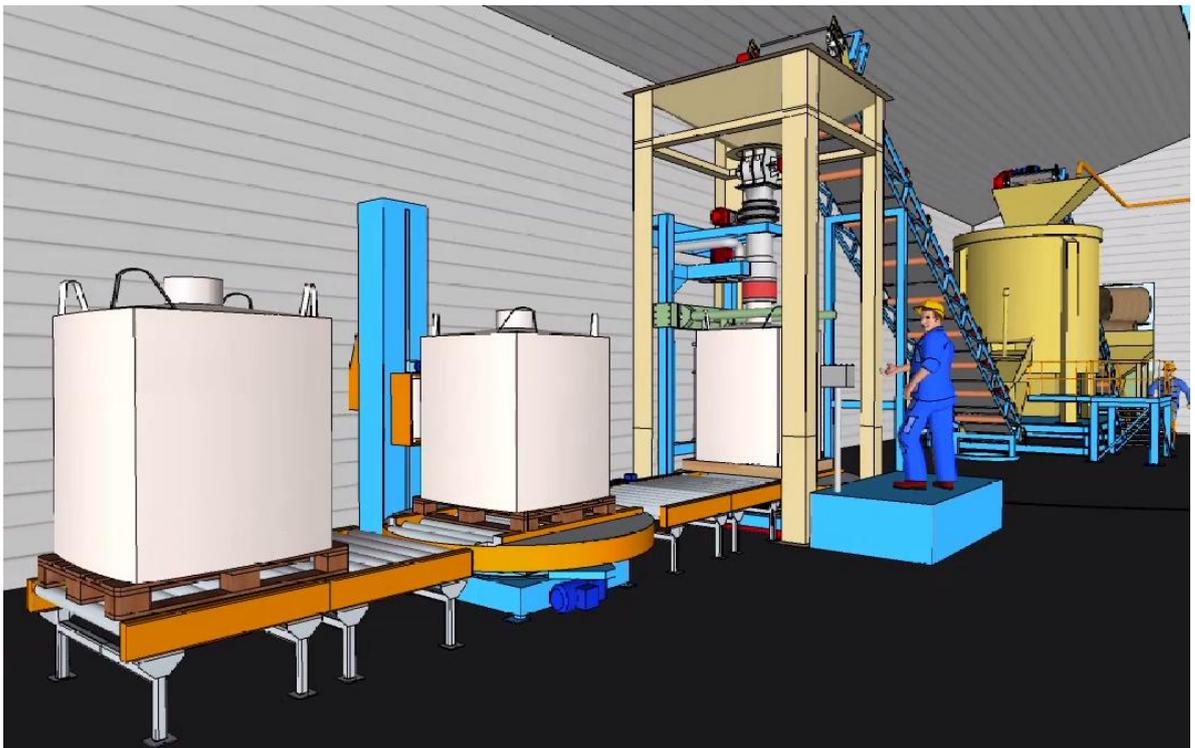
Общий вид фасовочного узла 11 для сыпучего почвообразователя в мягкие контейнеры
